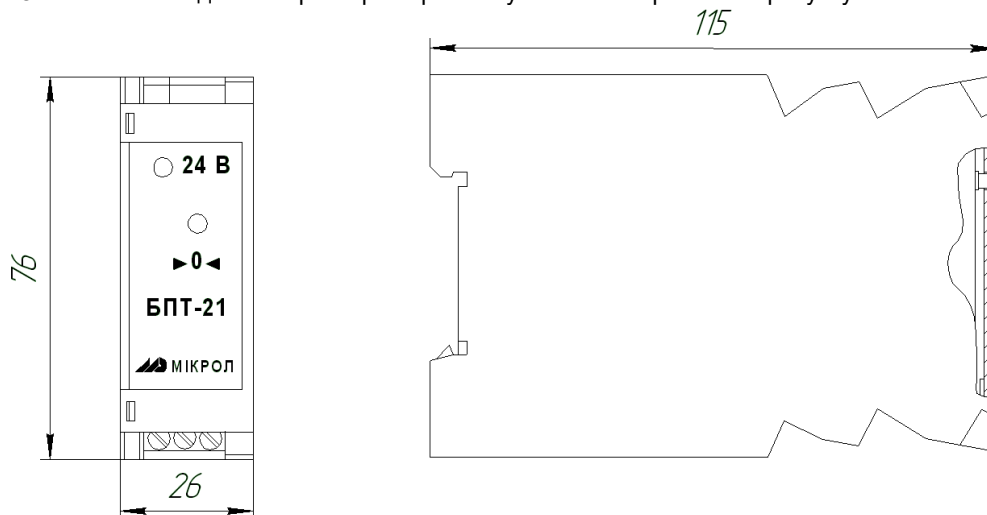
Зовнішній вигляд та габаритні розміри БПТ-21
